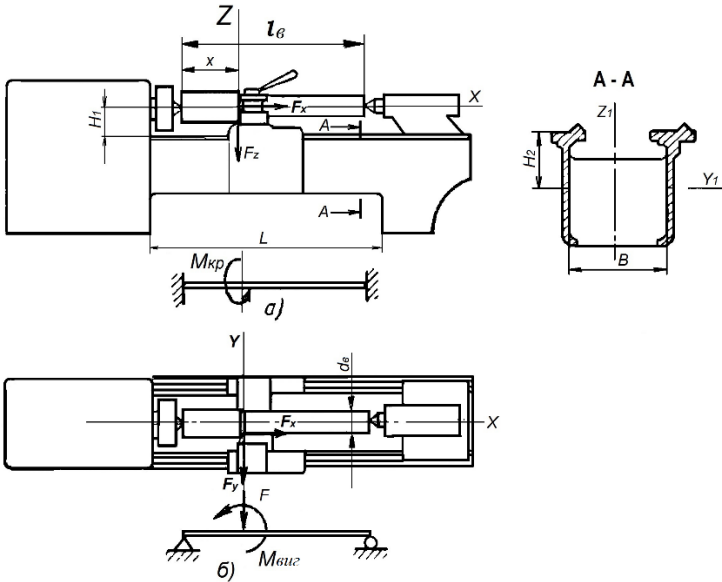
Розрахункова схема станини токарного верстата
